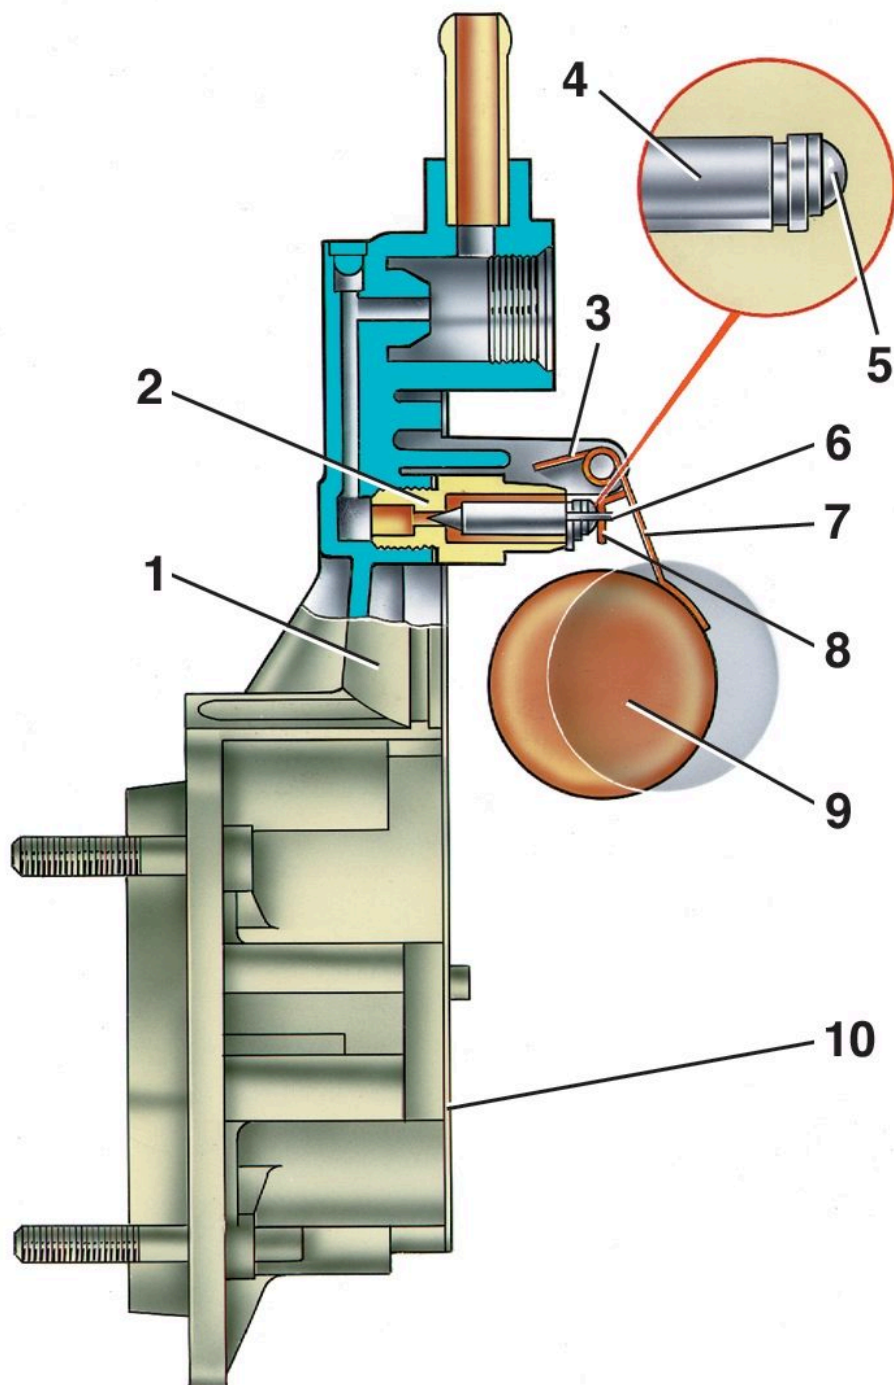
Установка рівня палива в поплавковій камері карбюратора: 1 - кришка карбюратора; 2 - сидло голчастого клапана; 3 - упор; 4 - голчастий клапан; 5 - кулька запірної голки; 6 - відтяжна вилка голки клапана; 7 - кронштейн поплавця; 8 - язичок; 9 - поплавець; 10 - прокладка
